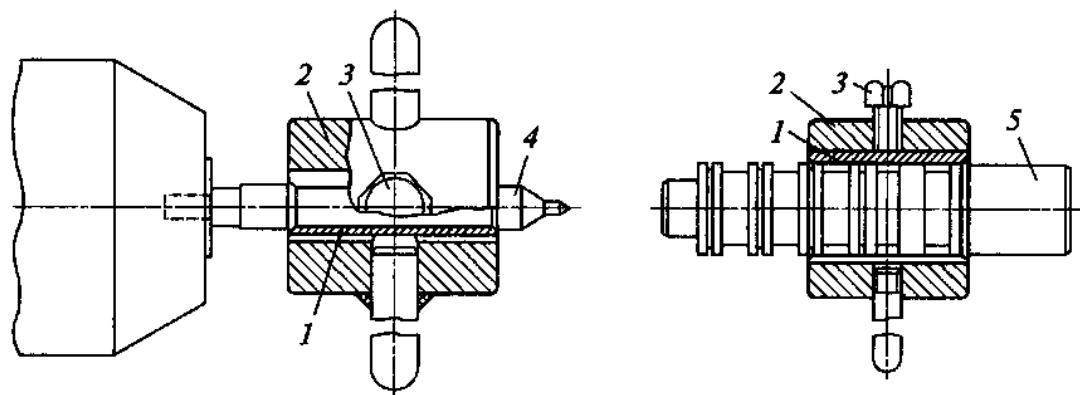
Притиры для доводки поверхностей охватываемых деталей:
